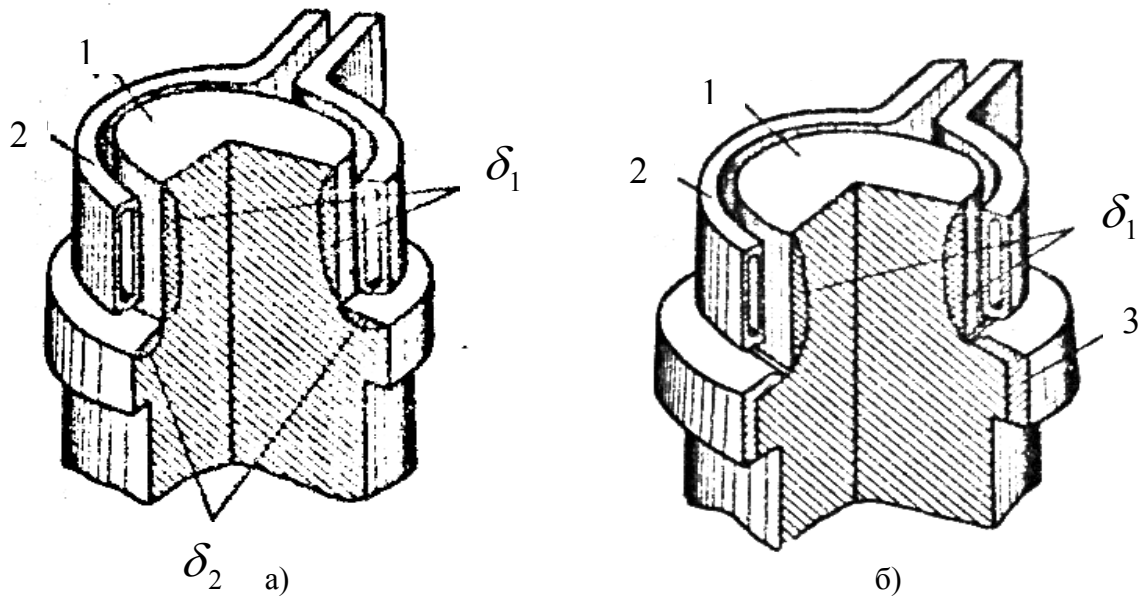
Форма нагрітого шару одновитковим індуктором на поверхні ший і виступі сталевого вала [11]:
